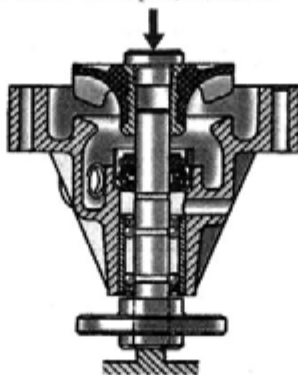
Напрессовка крыльчатки водяного насоса
